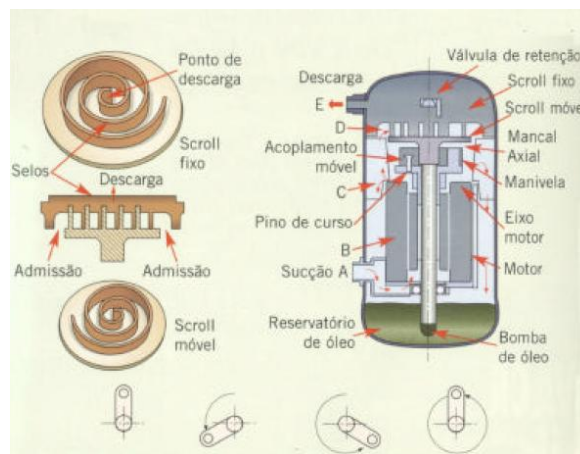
Compressor Scroll em corte (Trane, 2006)
